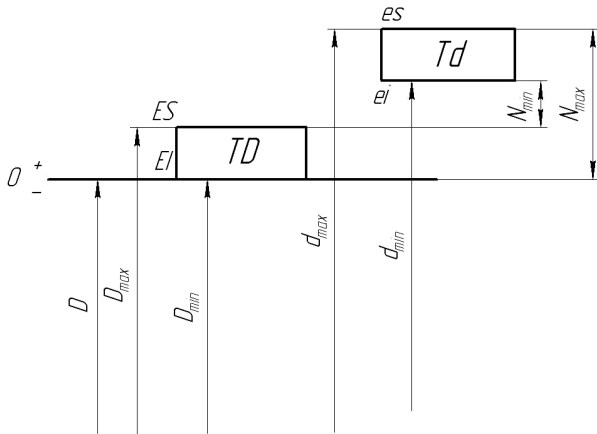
Схематичне зображення полів допусків посадки з натягом
